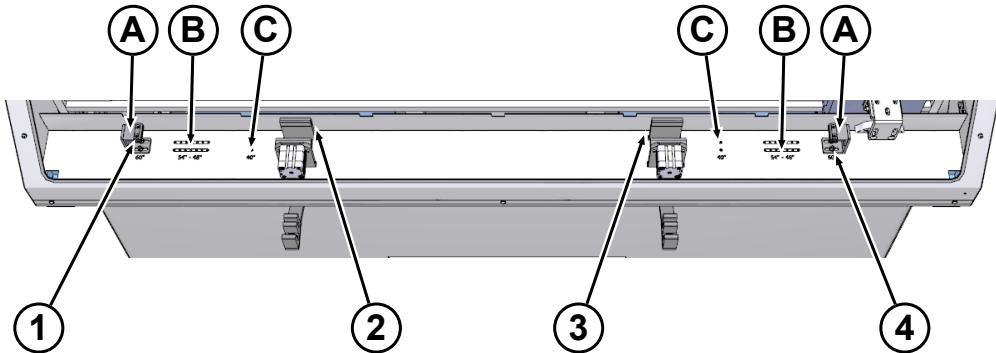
Possíveis posições dos suportes do chapéu de cardagem na área de ruptura
